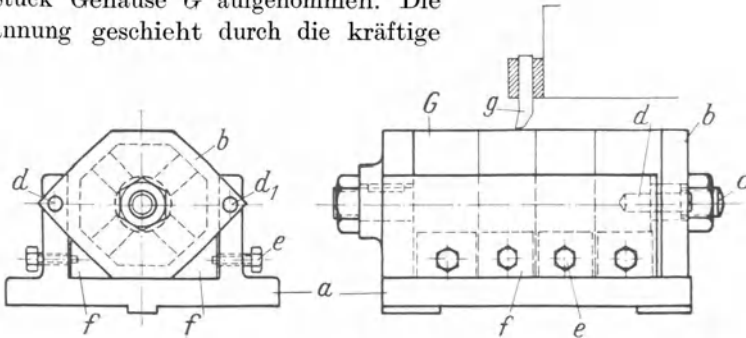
Hobelvorrichtung für das Abrichten von Spannflächen an Motorgehäusen.
